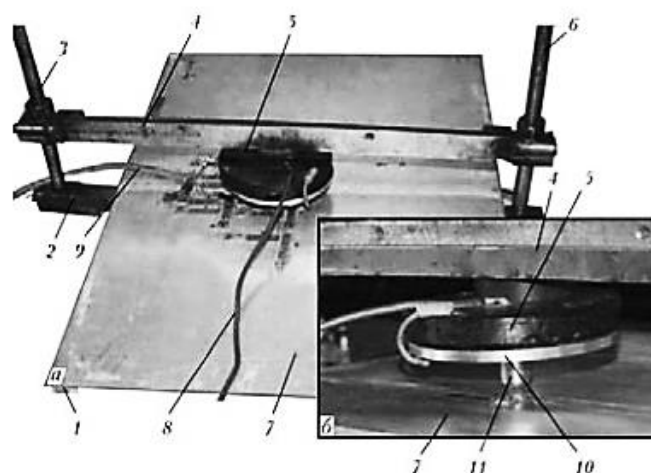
Внешний вид приспособления для ЭДО. 1 – подпятник; 2 – опорная балка; 3 – гайка; 4 – прижимная балка; 5 – плоский кондуктор; 6 – силовые шпильки; 7 – образец; 8 – силовой кабель; 9 – тензометрический шлейф; 10 – диск неферромагнитный; 11 – электрод.
